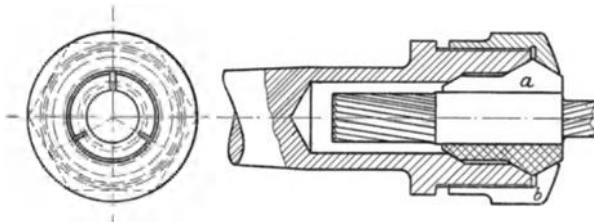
Das Klemmfutter für zylindrische Fräferschäfte.
